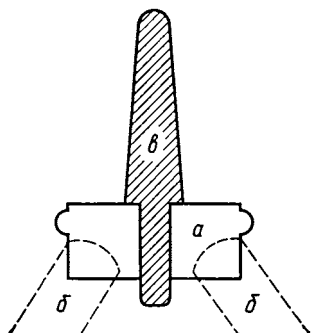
Приспособление для установки буссоли на штативе фотоаппарата
